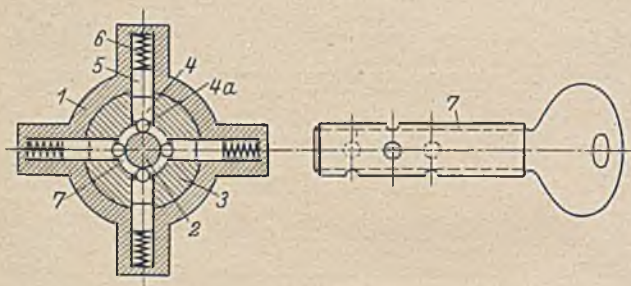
und 111. Schließzylinder mit Bohrungen im Schlüssel
